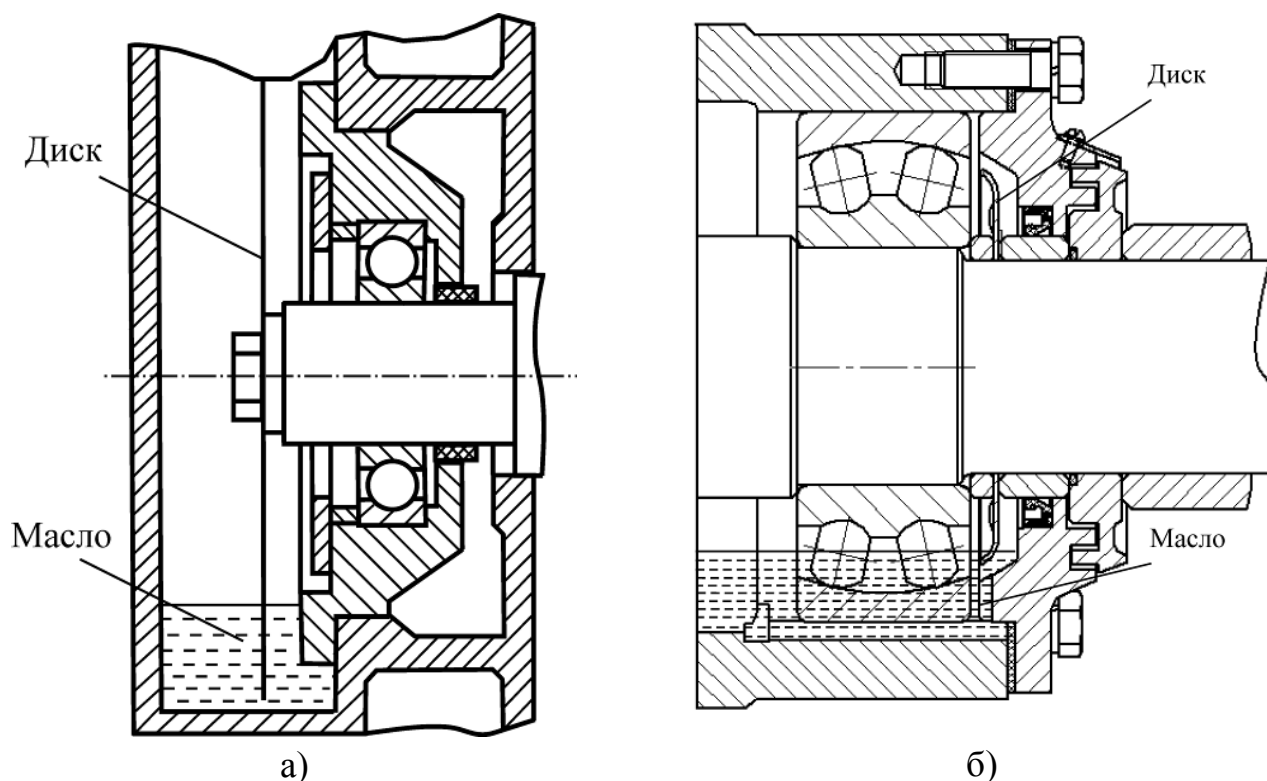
Конструкция смазки подшипникового узла ведомого вала:
